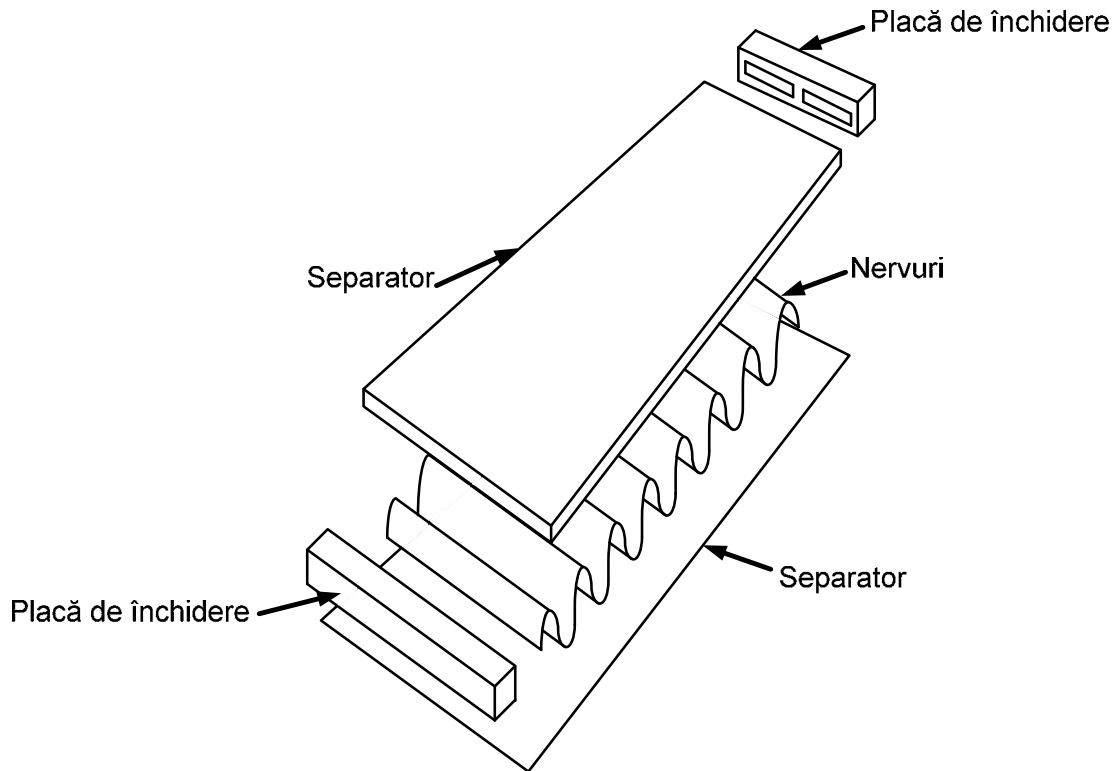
Elementele constructive ale unui schimbător de căldură cu plăci
